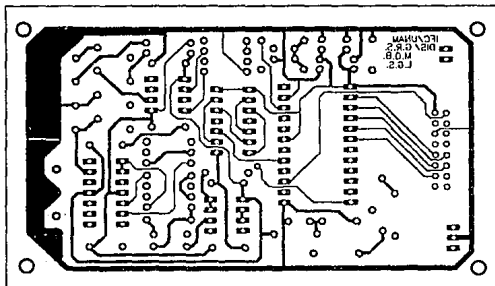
Cara de soldadura del circuito impreso de la etapa de adquisición
